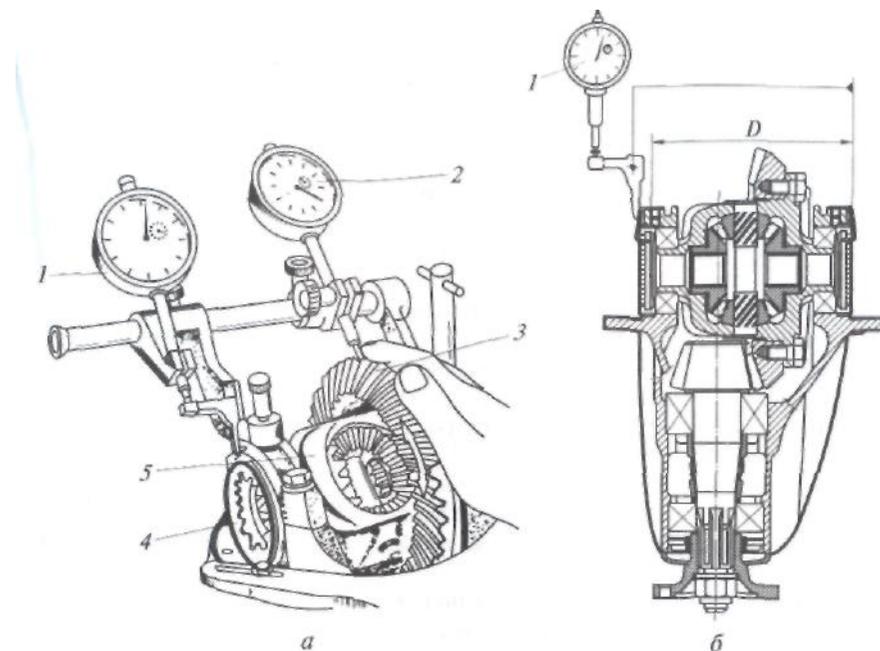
Схема регулирования зацепления зубьев колес главной передачи с помощью специального контрольного приспособления:
